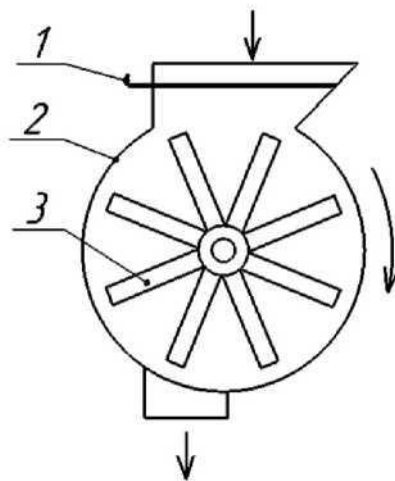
Барабанний дозатор: 1 – заслінка; 2 – корпус; 3 – лопатевої барабан
